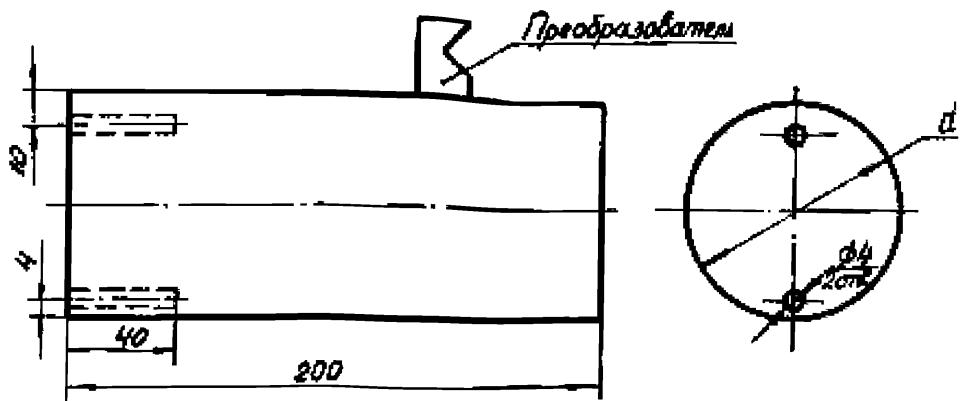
Стандартный образец для настройки ультразвукового прибора при НК штропов;
